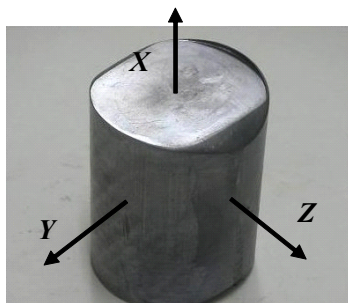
Форма поковки после завершения цикла обжатий литой заготовки
